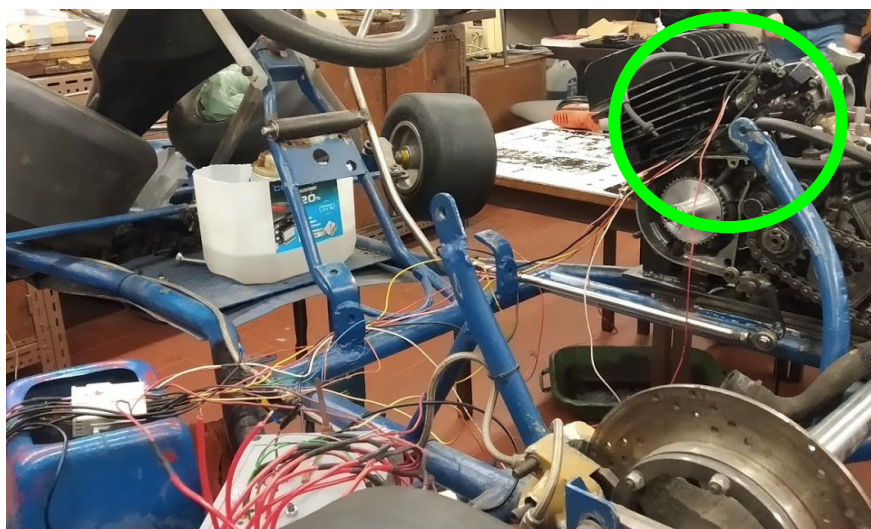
Processo de instalação da cablagem, estando rodeados a verde alguns dos componentes já soldados.
